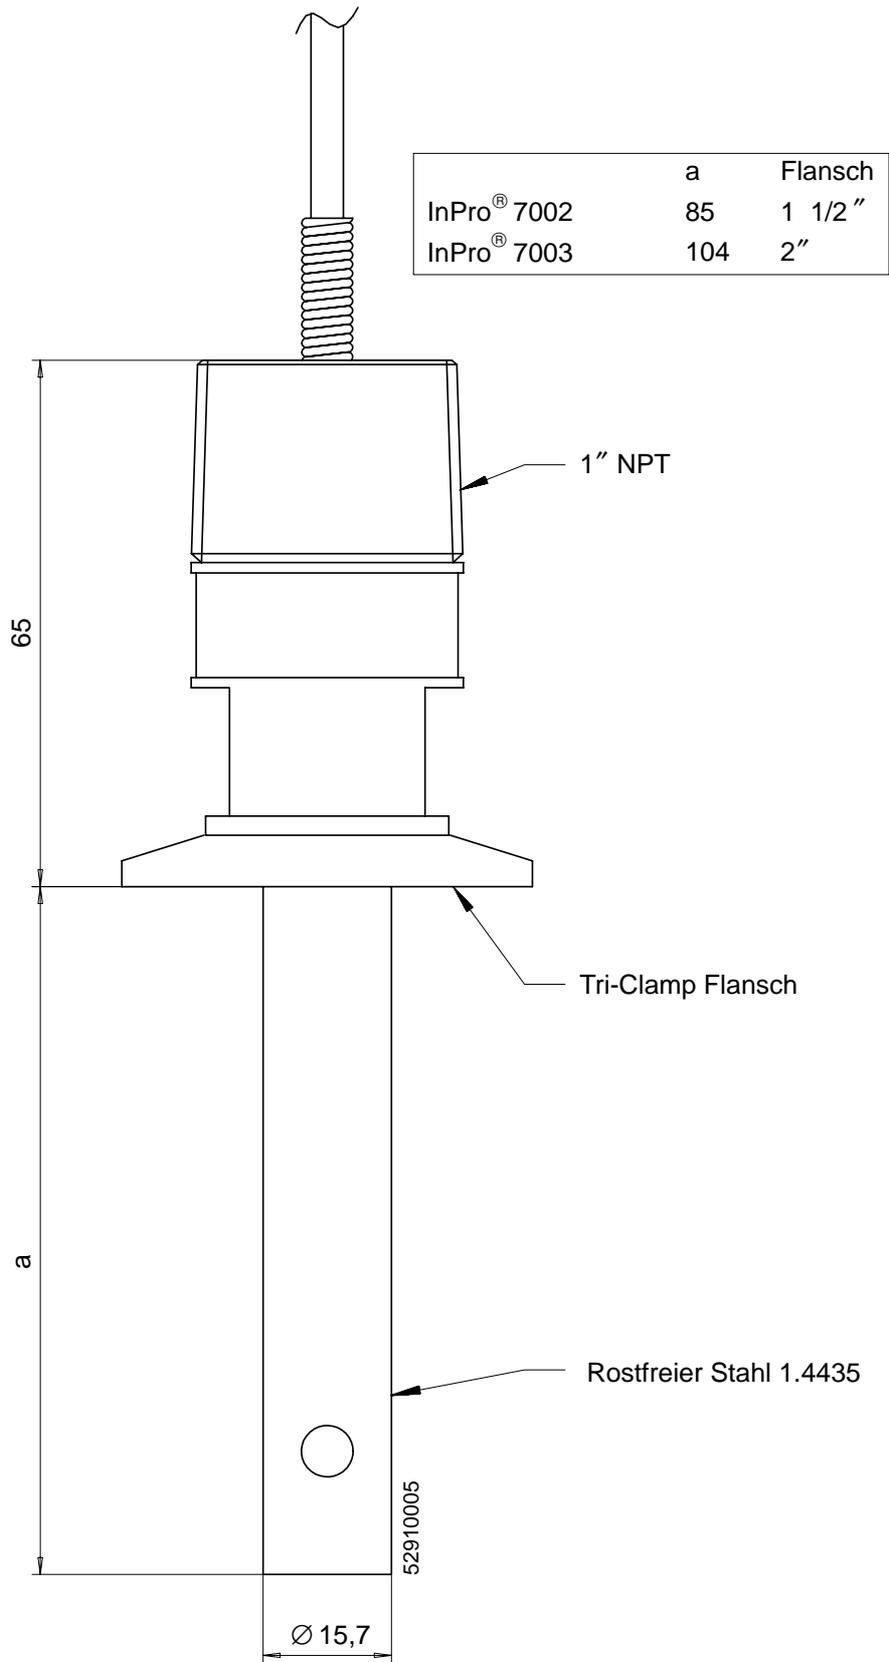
Maßzeichnung InPro[®] 7002 / 7003
